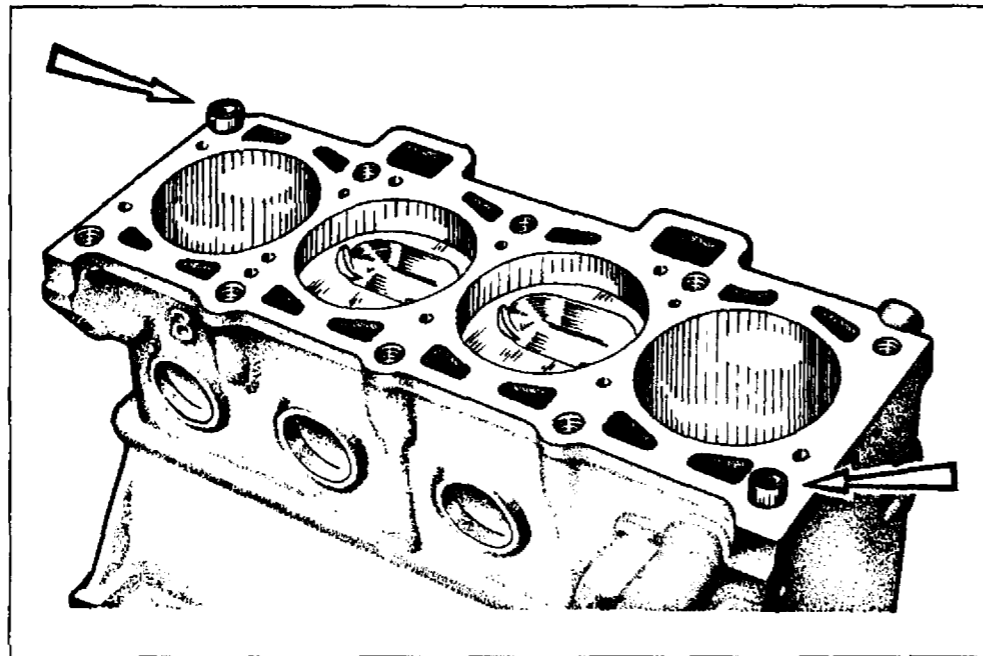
Втулки для центрирования головки на блоке цилиндров
